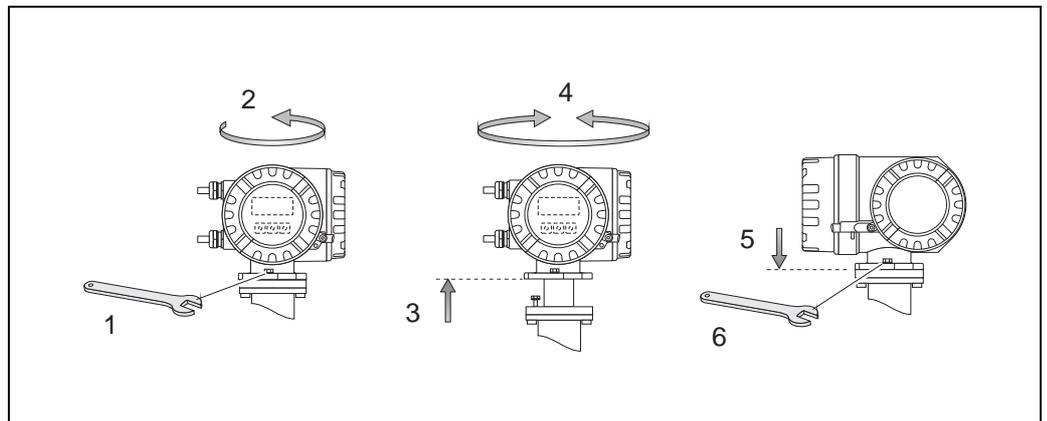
Drehen des Messumformergehäuses (Aluminium-Feldgehäuse)
